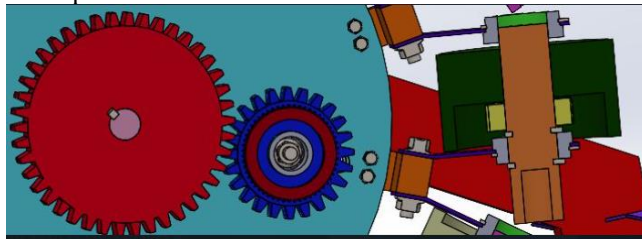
Engranajes en pieza 5 y al tren de movimiento superior
